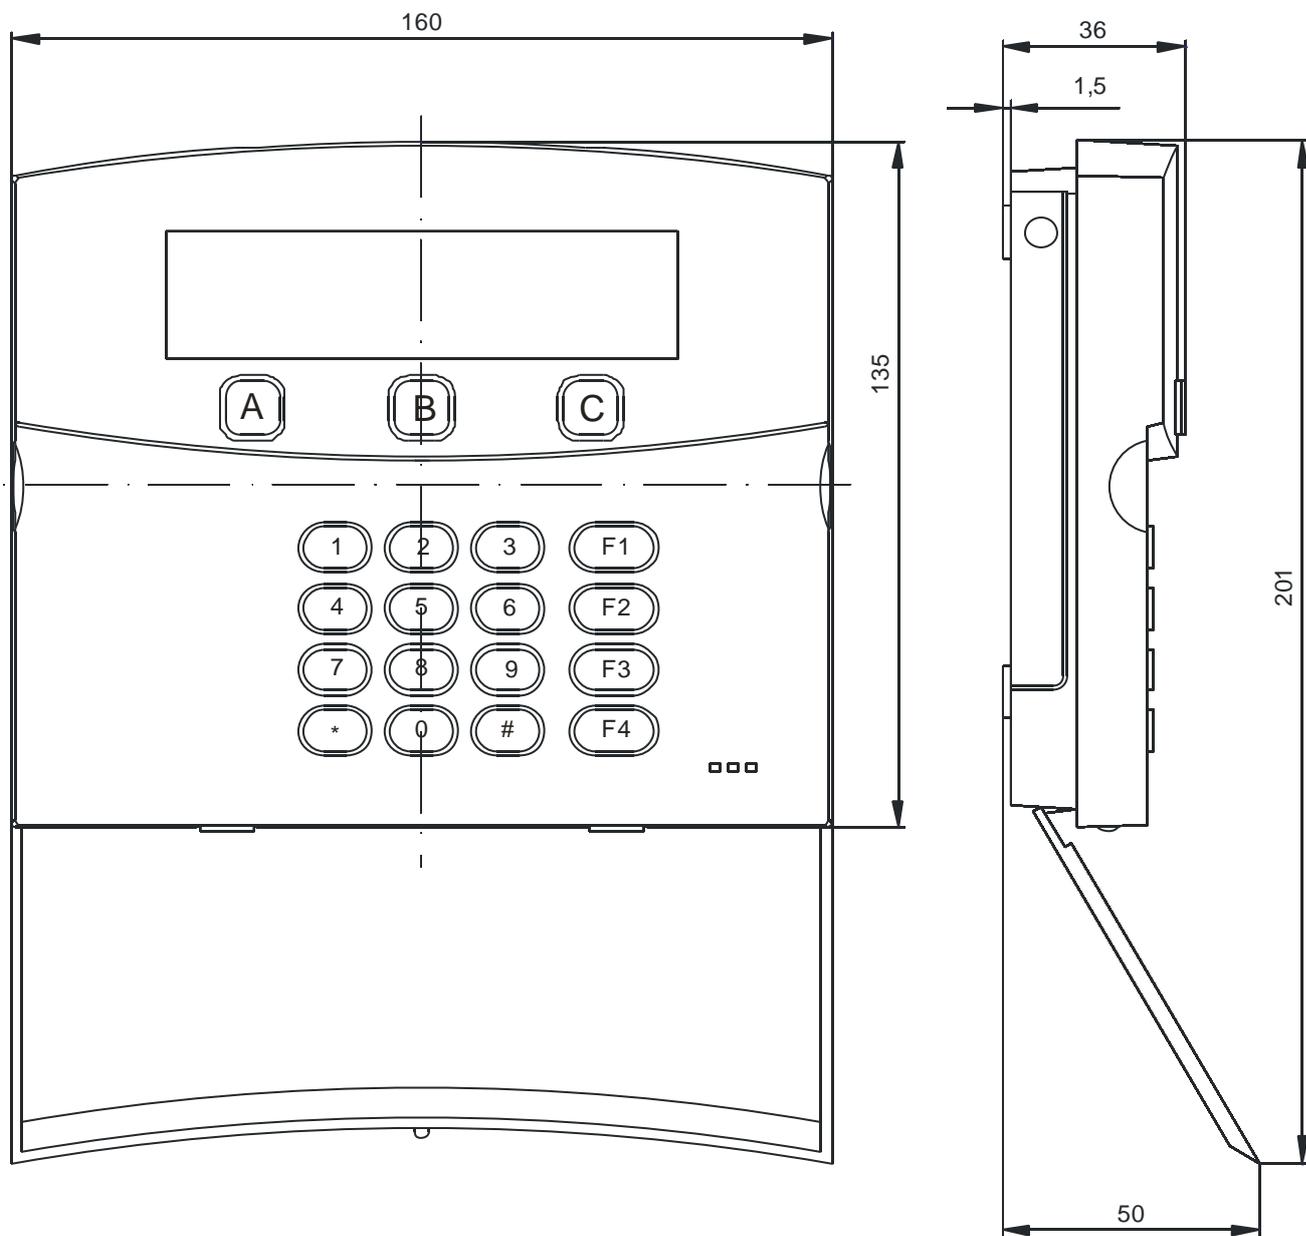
Габаритный чертеж корпуса (крышка откинута).
